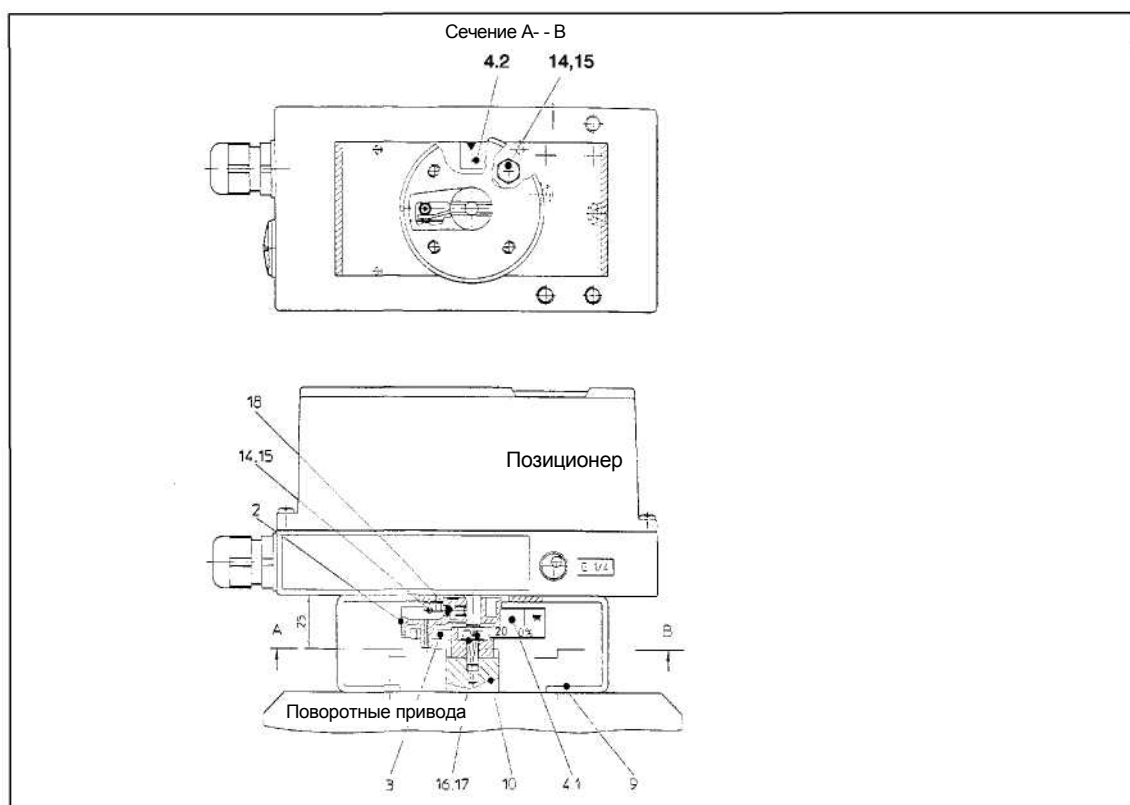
Процедура сборки для взрывонепроницаемой версии (поворотный привод)
